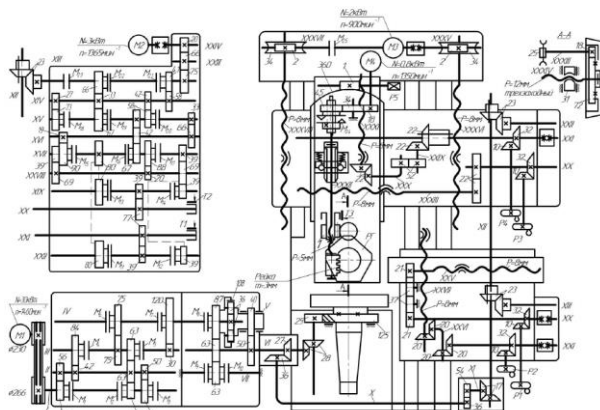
Кинематическая схема главного движения токарно-карусельного станка 1512
